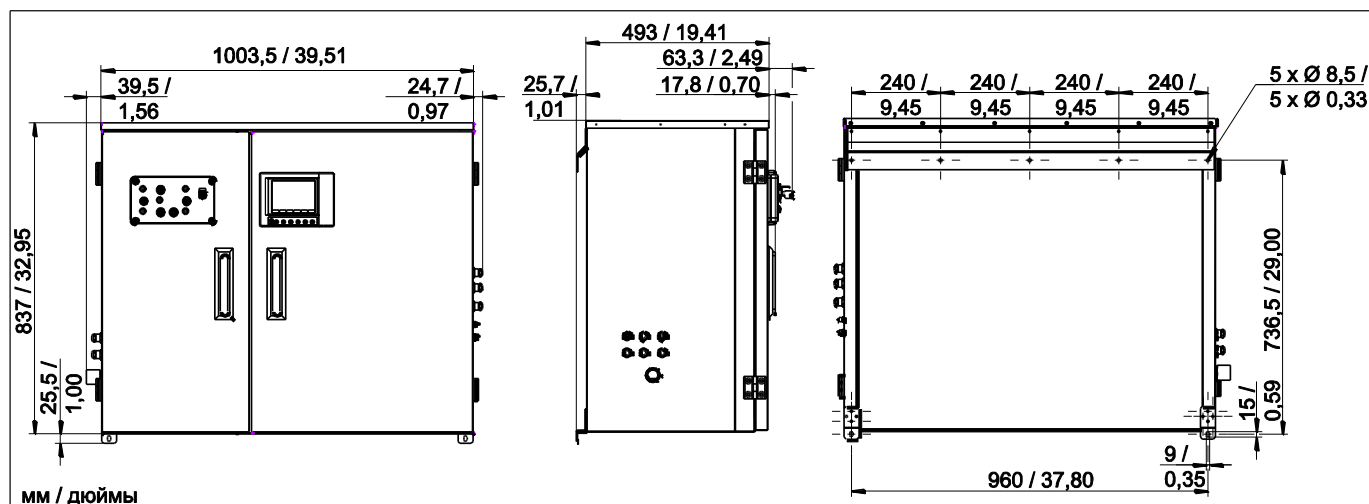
Размеры корпуса CYC300, исполнение из нержавеющей стали
